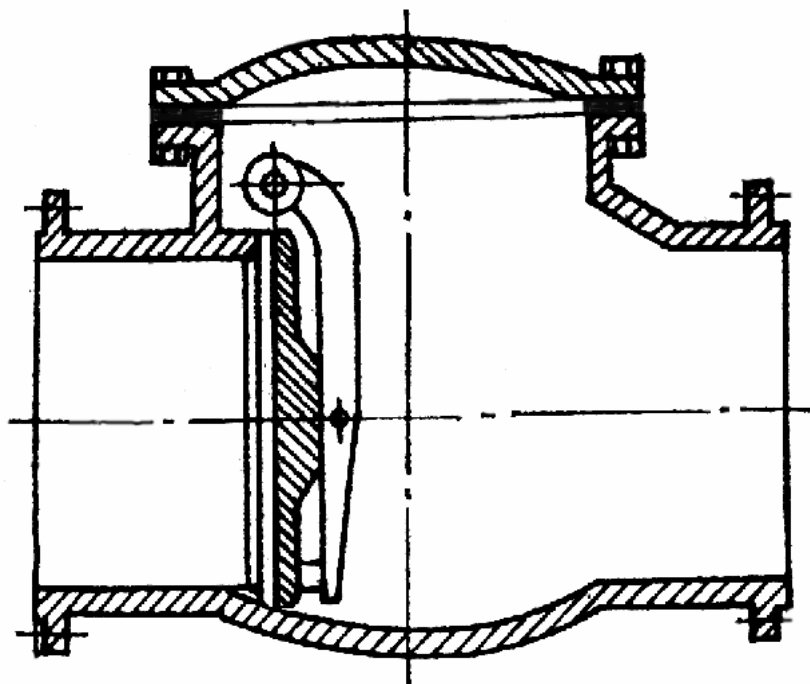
Клапан обратный поворотный однодисковый фланцевый
